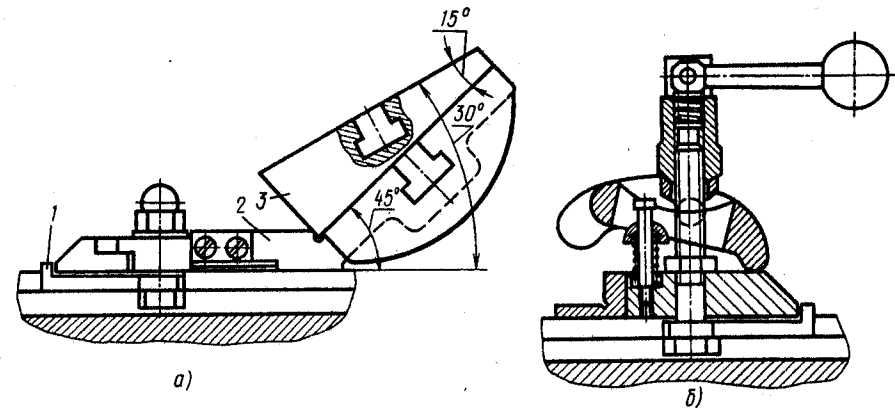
Приспособления для закрепления резцов на заточном станке мод. 3622
